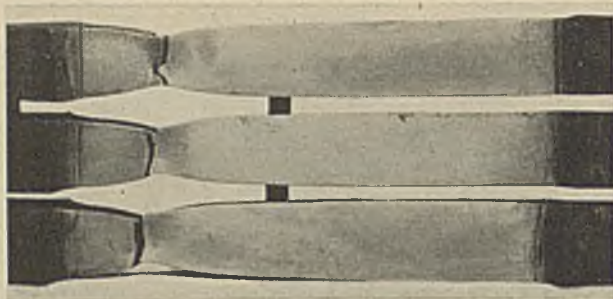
Zerreißproben von Schweißnähten (Blechstärke 45 mm).
